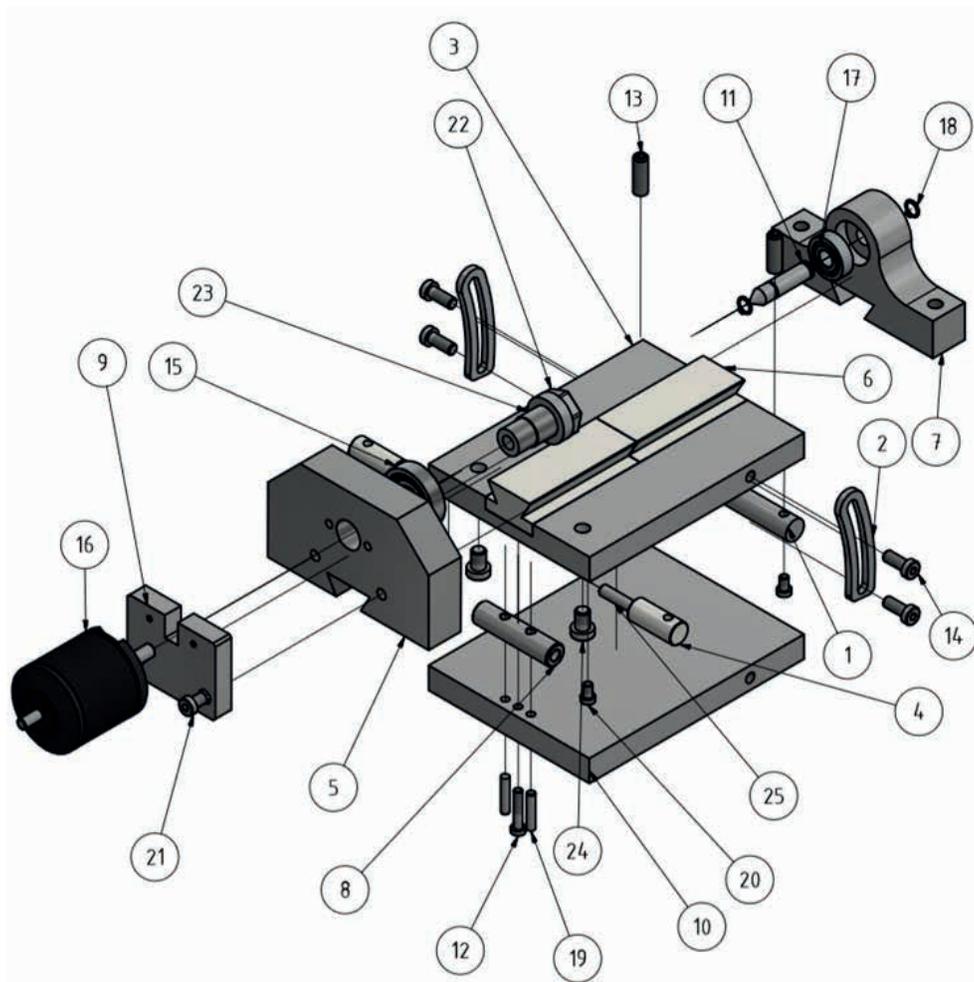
Vista explodida do dispositivo de adaptação de retíficas planas para usinagem de peças cilíndricas
